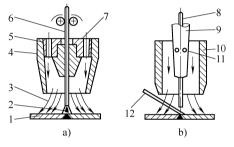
CO, 气体保护焊焊接设备及附件
